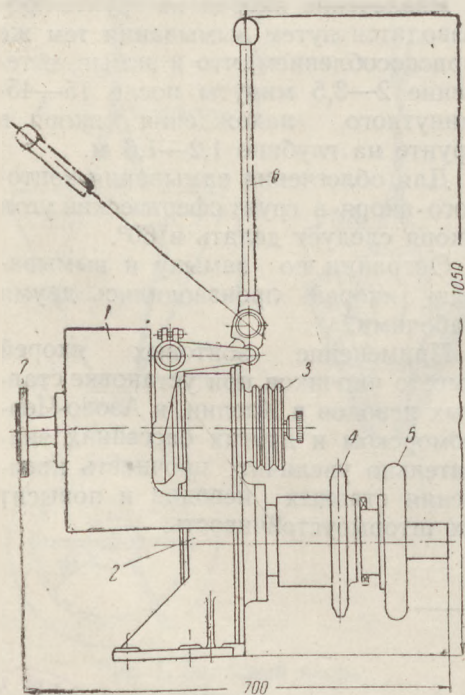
Устройство для отбора мощности от двигателя ЗД6.
